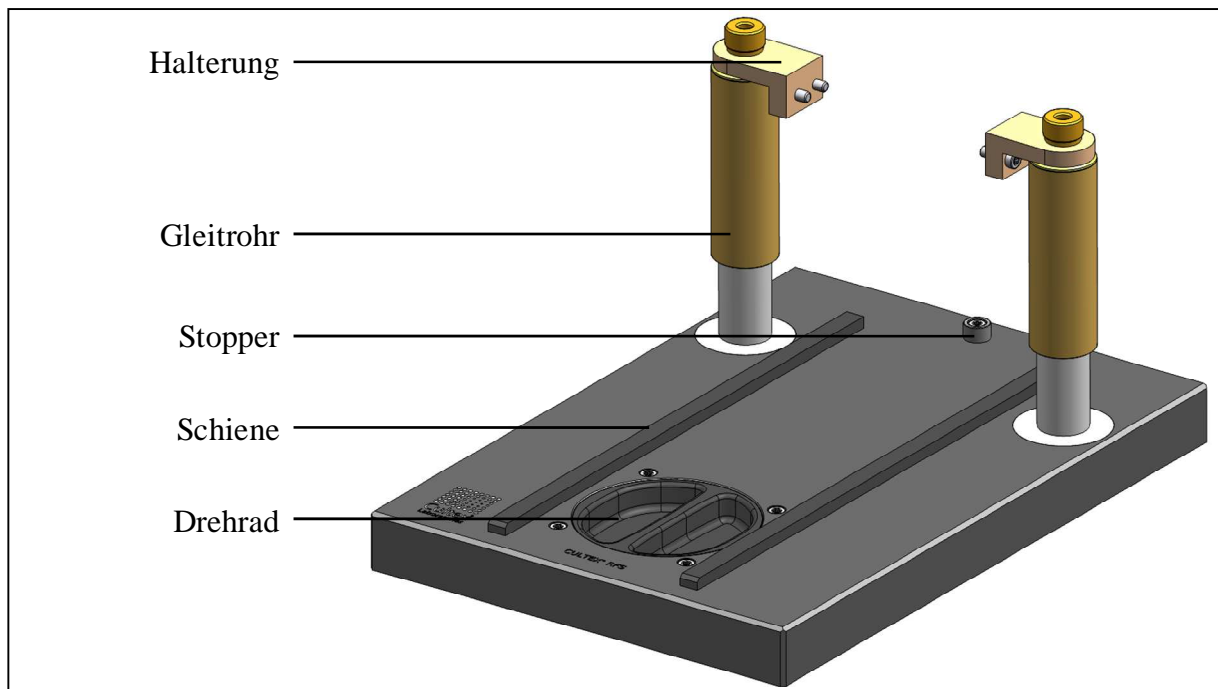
Hebevorrichtung. (Zeichnung: Halter Engineering GmbH)
